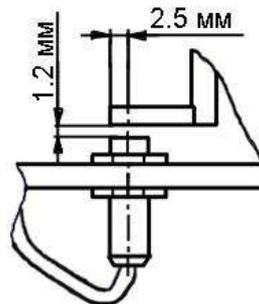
Регулировка датчика положения бруска абразивного
